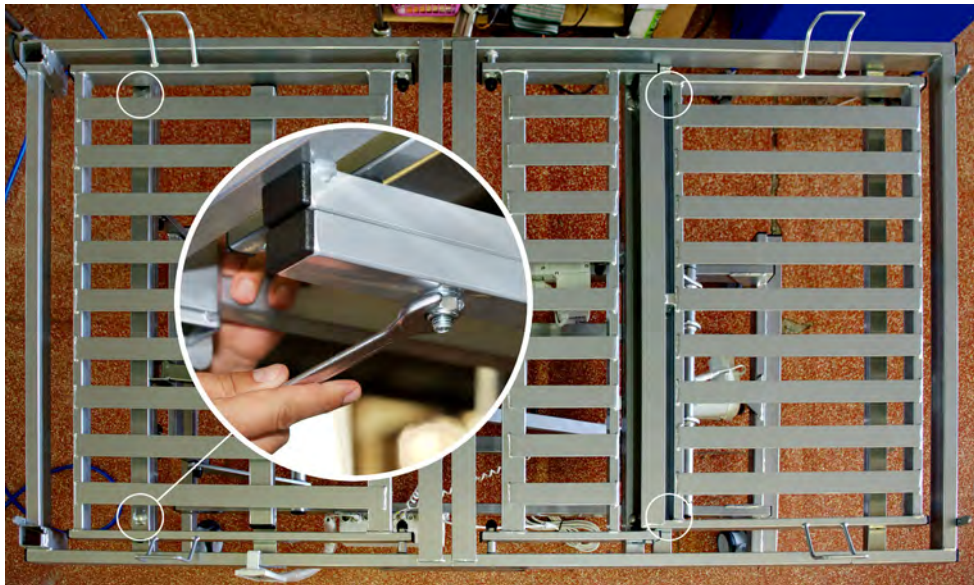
An diesen vier Punkten die Verschraubung der Liegefläche lösen.
